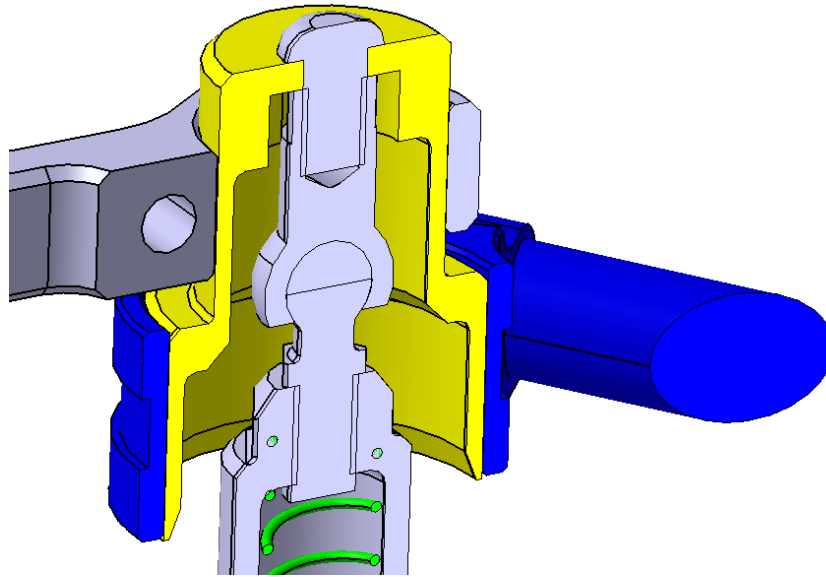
Corte de la pieza MT2-DI-00-03 en su montaje final.
